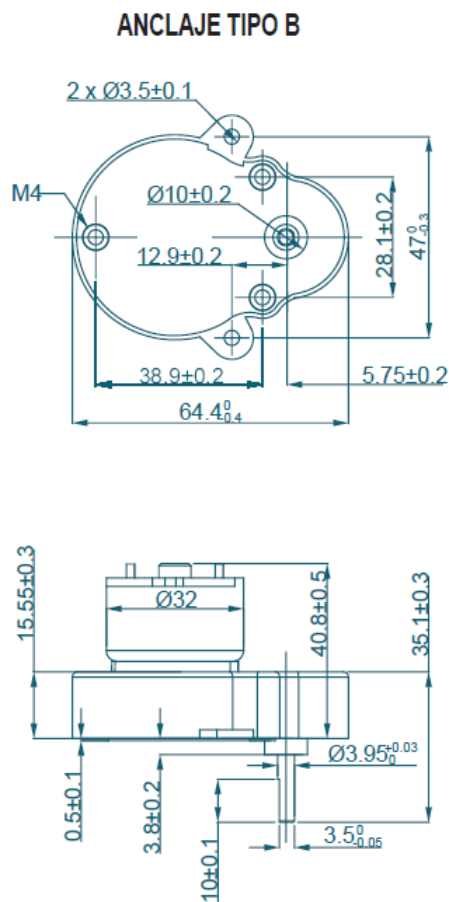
Dimensiones moto reductor (fuente CLR)
